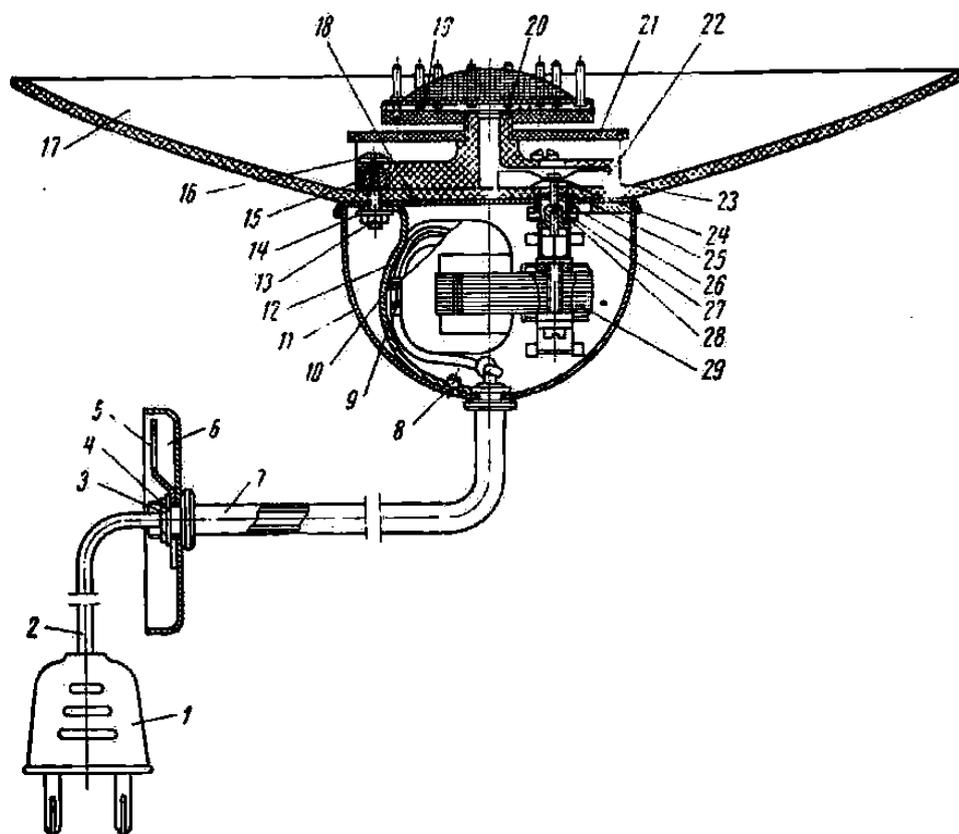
Увлажнитель воздуха УВ-1; 1 - штепсельная вилка; 2 - соединительный шнур; 3, 24, 28 - специальные гайки; 4, 14, 21, 25 - шайбы; 5 - скоба; 6, 18 - колпачки; 7 - трубка; 8, 16 - винты; 9 - изоляция; 10 - хлорвиниловая трубка; 11 - колпак; 12 - кронштейн; 13 - гайка; 15 - специальный винт; 17 - диск; 19 - распылитель; 20 - фланец; 22 - кольцо; 23 - вентилятор; 26 - сальник; 27 - обойма; 29 - электродвигатель
